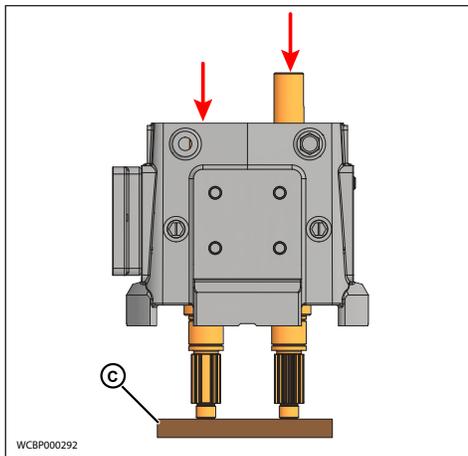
Herausdrücken der Wellen aus dem Getriebegehäuse
